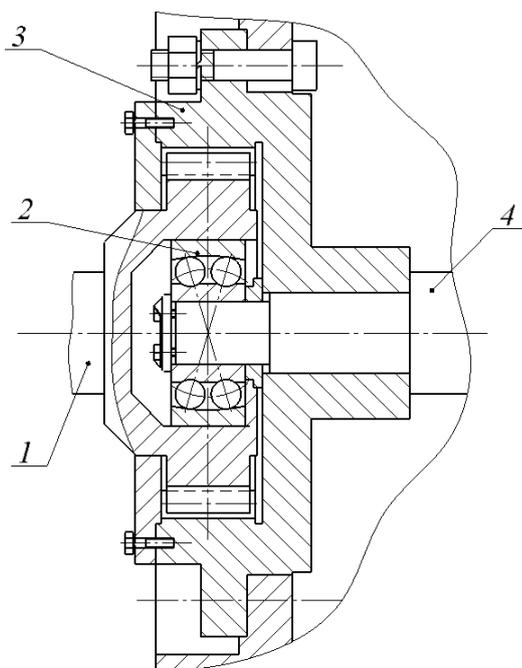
Схема соединения барабана с редуктором: 1 – тихоходный вал редуктора с концом, выполненным в виде зубчатой полумуфты; 2 – внутренний подшипник; 3 – зубчатая полумуфта; 4 – ось барабана
